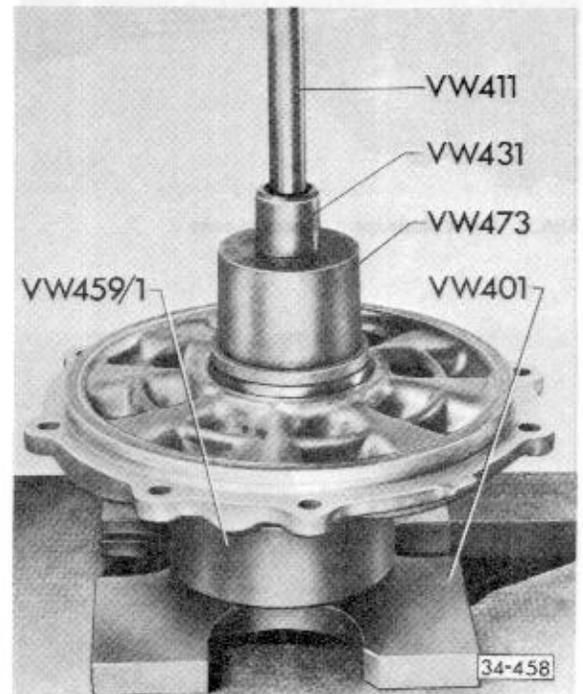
Außenring/Kegelrollenlager für Ausgleichgetriebe einpressen
